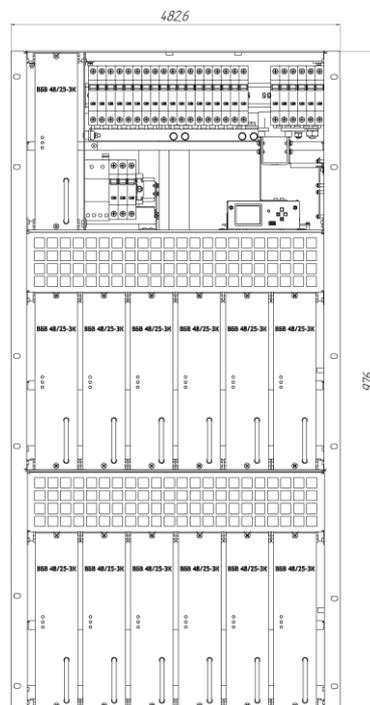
Габаритный чертеж УЭПС-3К 60/260, УЭПС-3К 48/325
